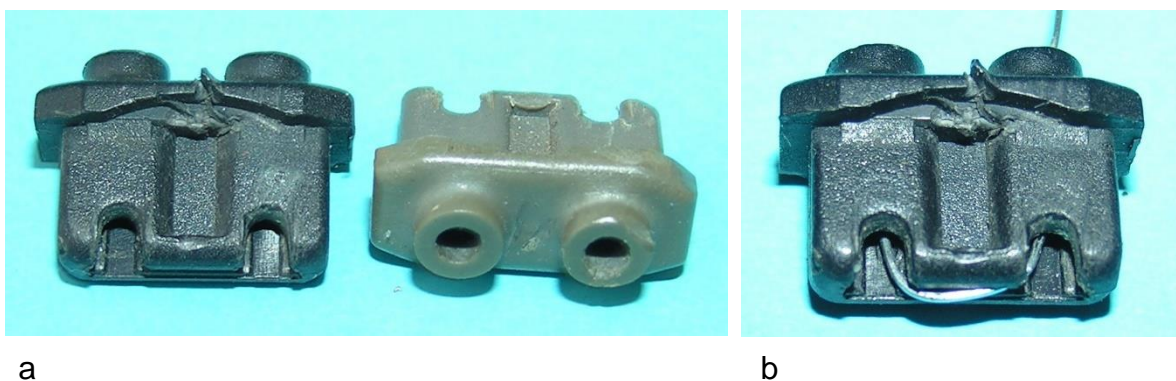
a) Kabeladapter, b) Eingefädelttes Kabelende
